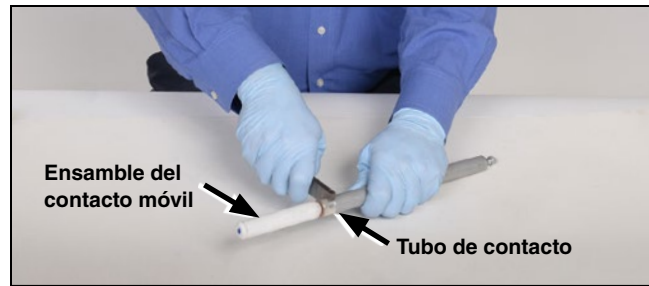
Instale el tubo de contacto en el ensamble del contacto móvil.
